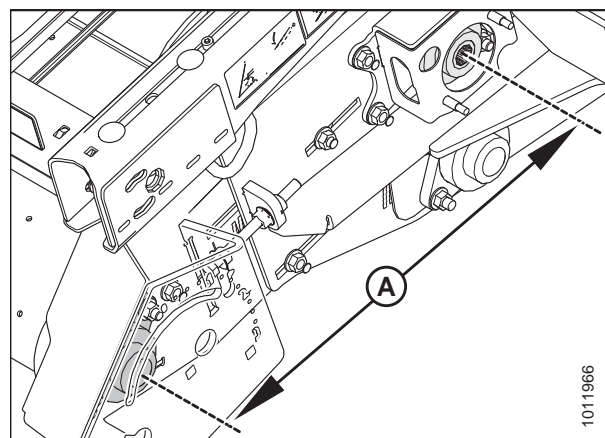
Регулировочное расстояние подшипника — левая сторона жатки
